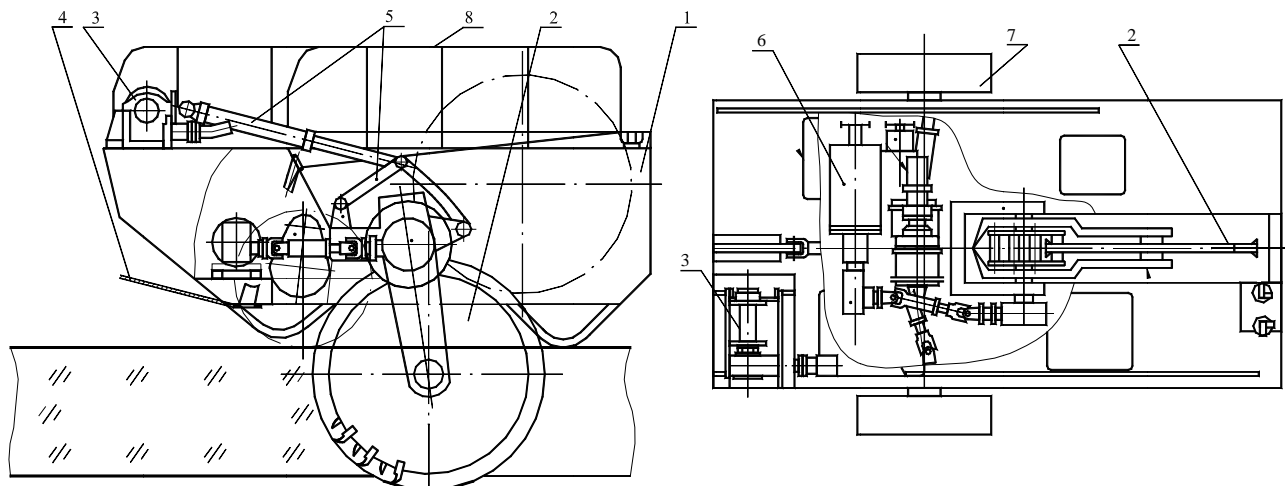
Схема дискофрезерной плавающей машины ЛФМП-1: 1 – несущий корпус-пonton; 2 – дисковая фреза; 3 – буксирная лебедка для выхода из воды на лед; 4 – буксирный трос; 5 – механизм подъема фрезы из рабочего положения в транспортное; 6 – электродвигатель привода фрезы, колес, лебедки; 7 – движители; 8 – леерное ограждение
